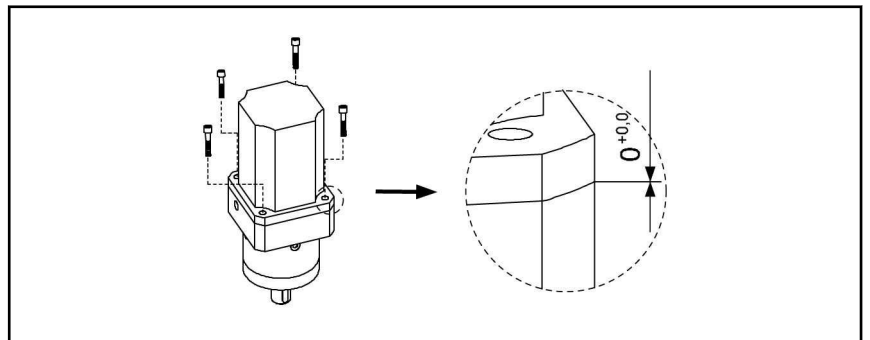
Anziehen der Motorbefestigungsschrauben (über Kreuz)
